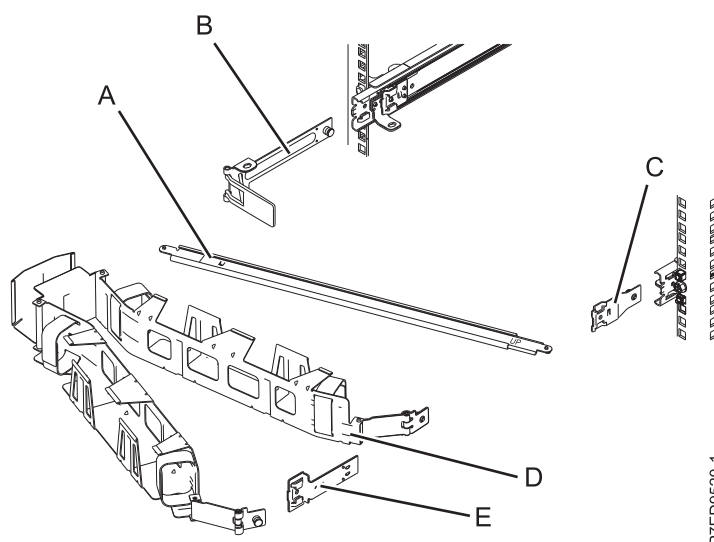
Posiciones relativas de las partes del brazo portacables antes del ensamblaje
